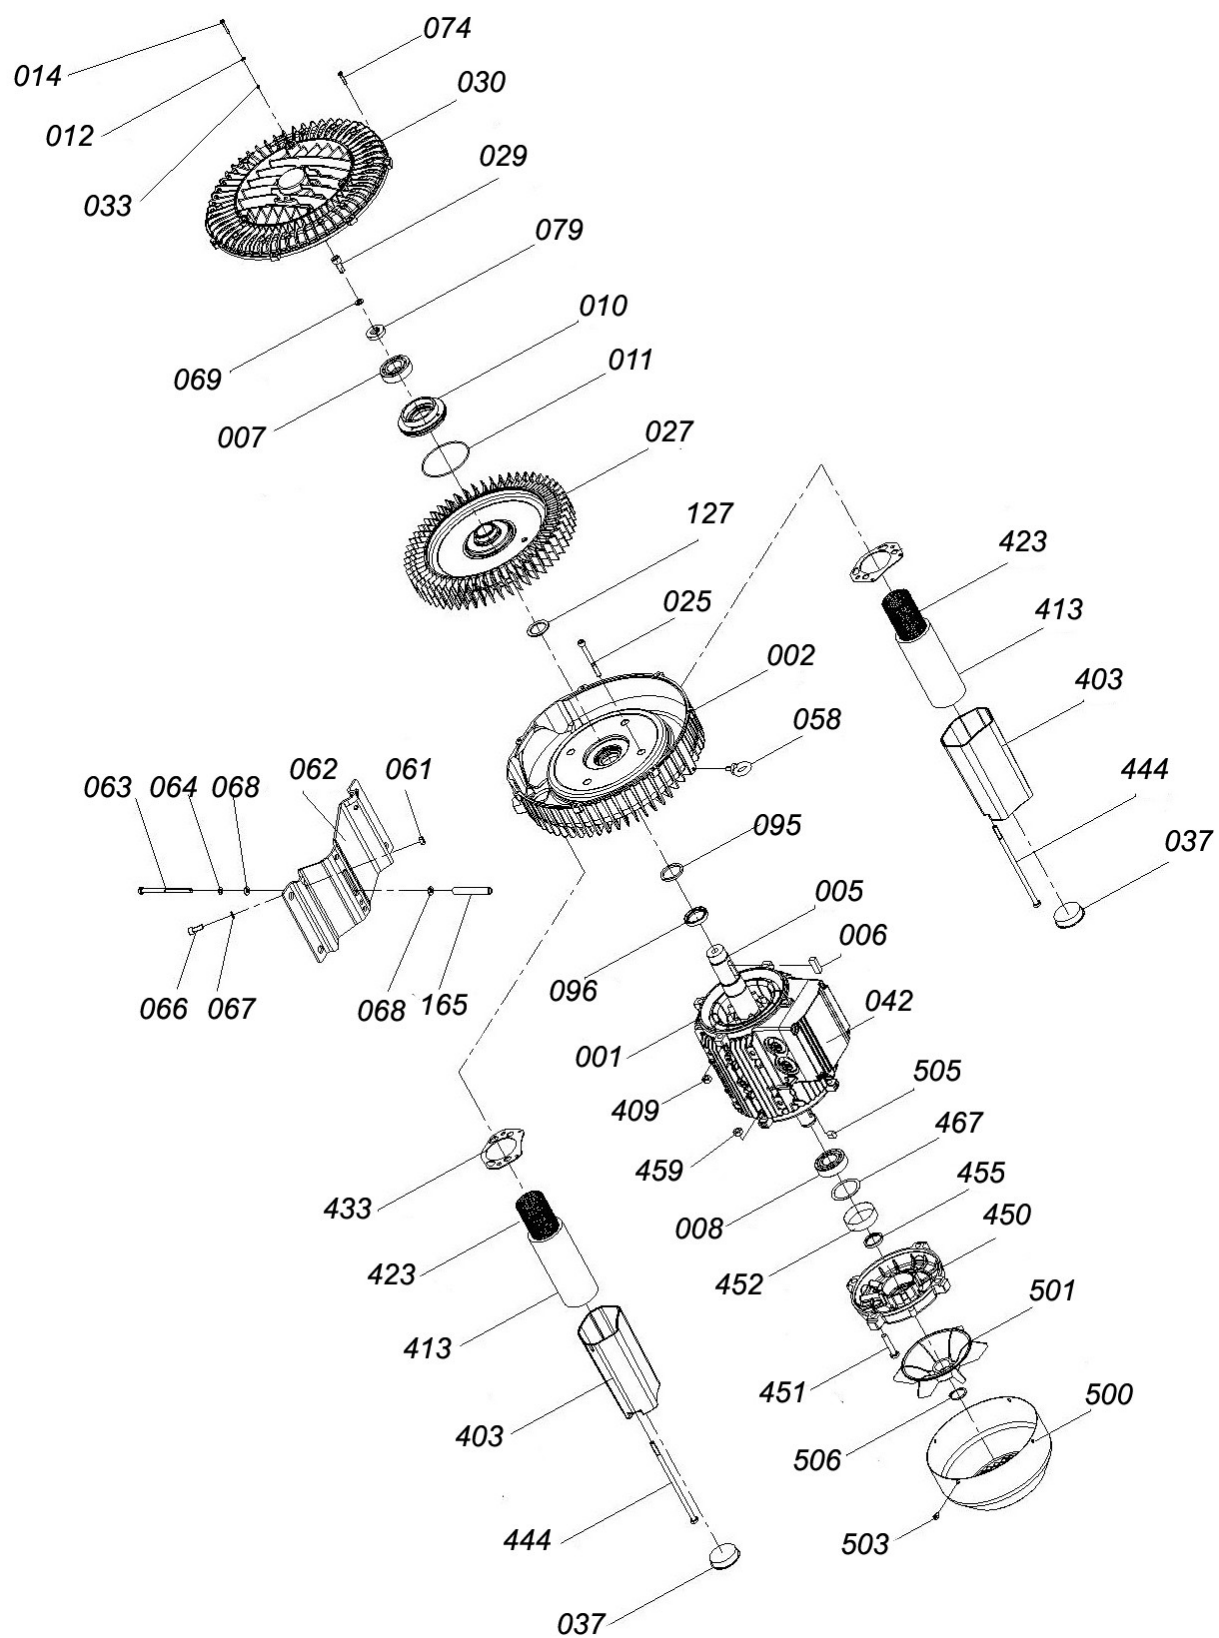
Детализовка одноступенчатых воздуховок 2RB
